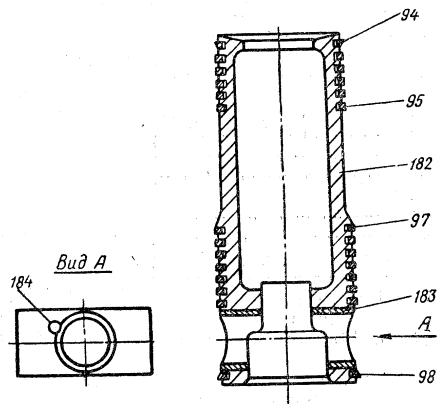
Узел крепления трубопровода первой ступени к головке.
